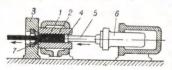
Схема прямого прессования на гидравлическом прессе: 1 — заготовка; 2 — контейнер; 3 рама; 4 — пресс-шайба; 5 — пуан-сон; 6 — плунжер; 7 — матрица.
